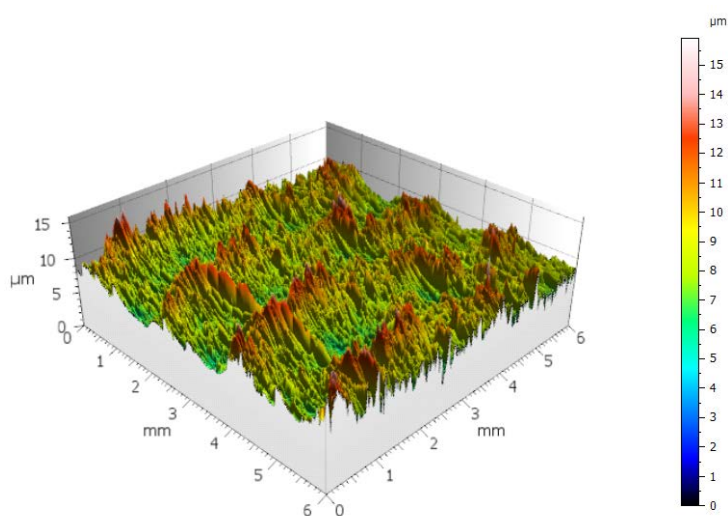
Топографія обробленої поверхні після фрикційної обробки інструментом з хвилеподібною робочою поверхнею
